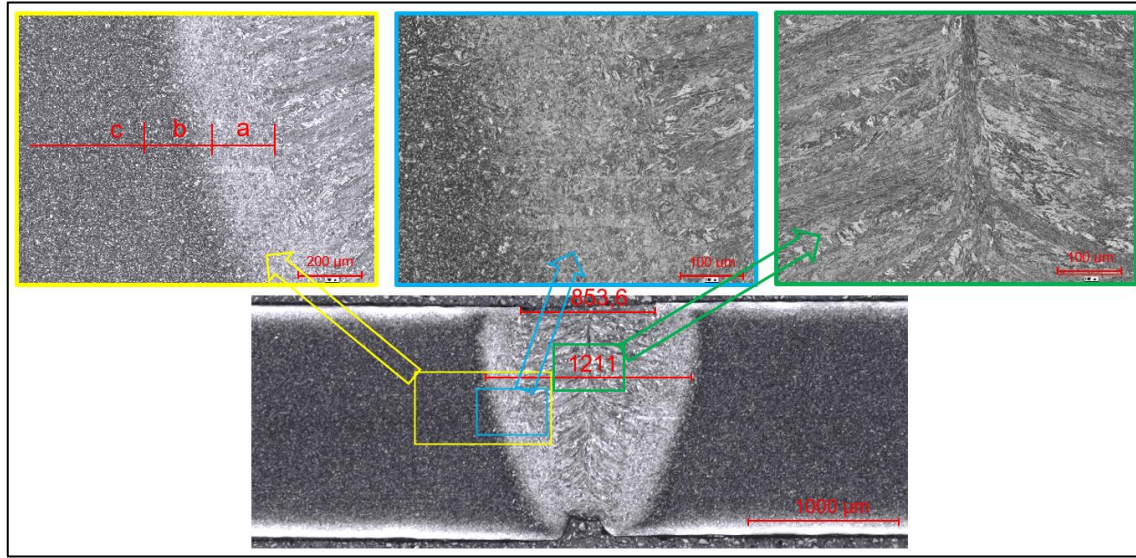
100 mm/sn hızla yapılan birleştirme (Welded sample joined with 100 mm/sec welding speed).
